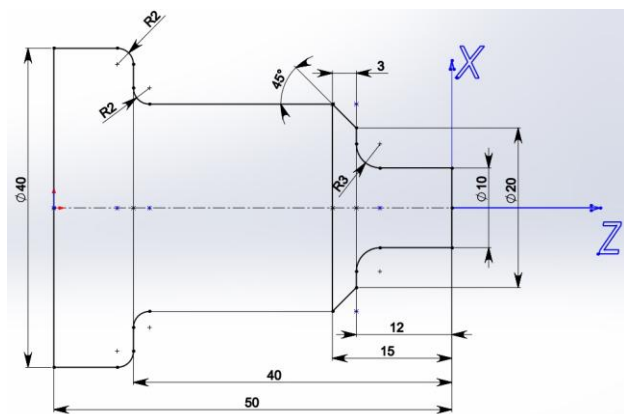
Опорні точки деталі за токарного оброблення
